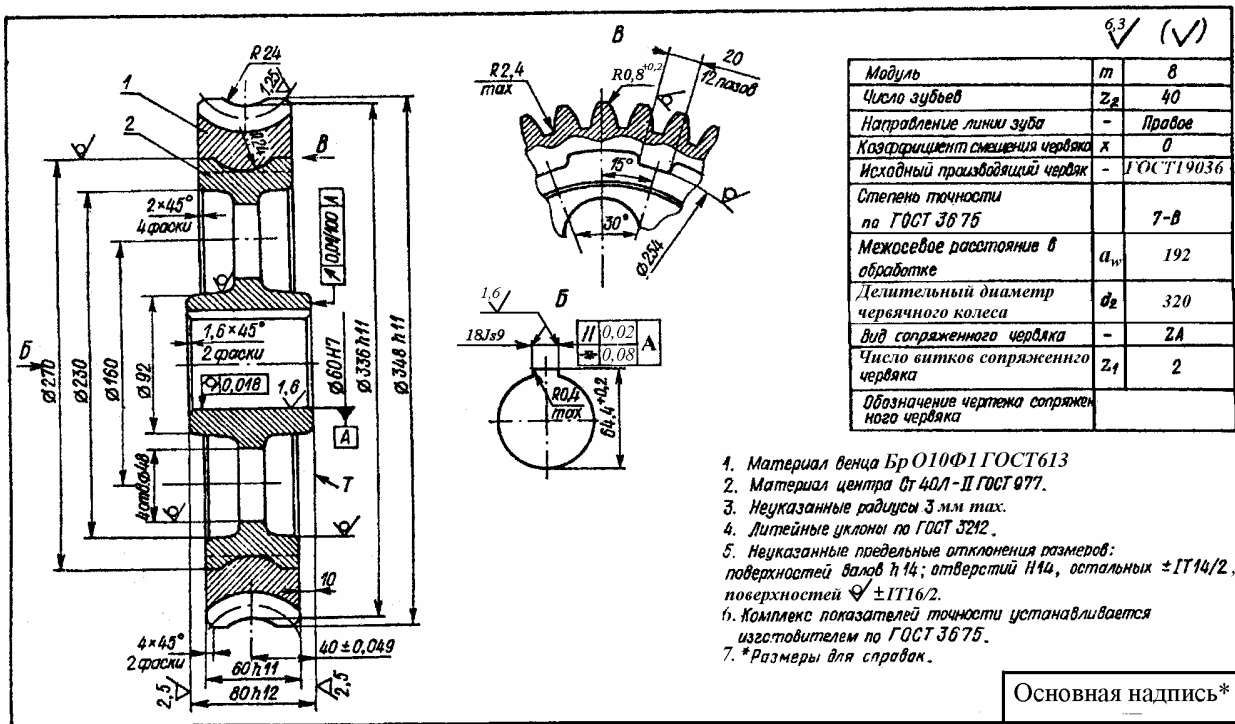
Рабочий чертеж червячного колеса в сборе
